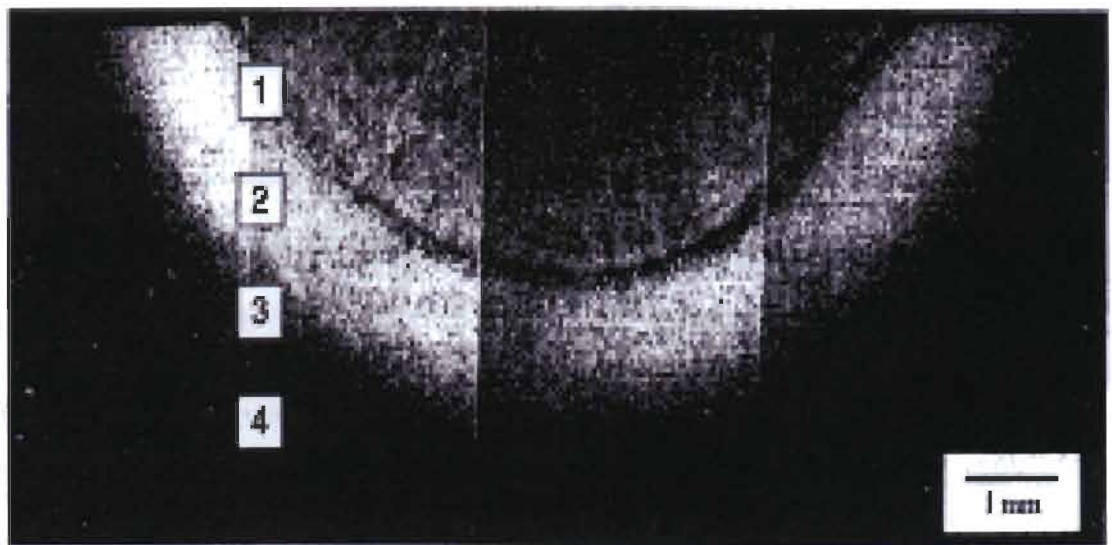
Regiones de ZAC de una soldadura GTAW
